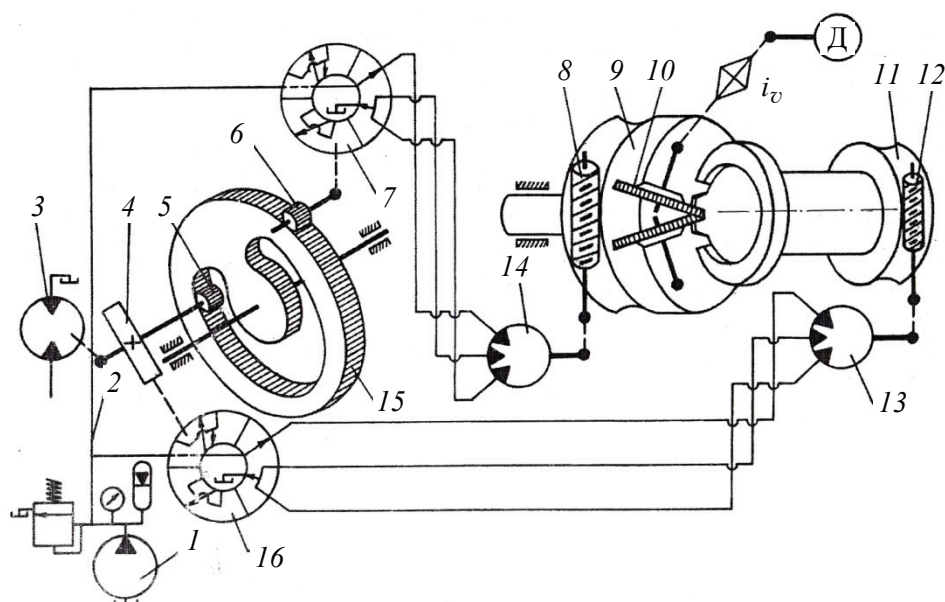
Структурная схема зуборезного станка с гидравлическими внутренними связями для нарезания прямозубых конических колес двумя резцовыми головками
